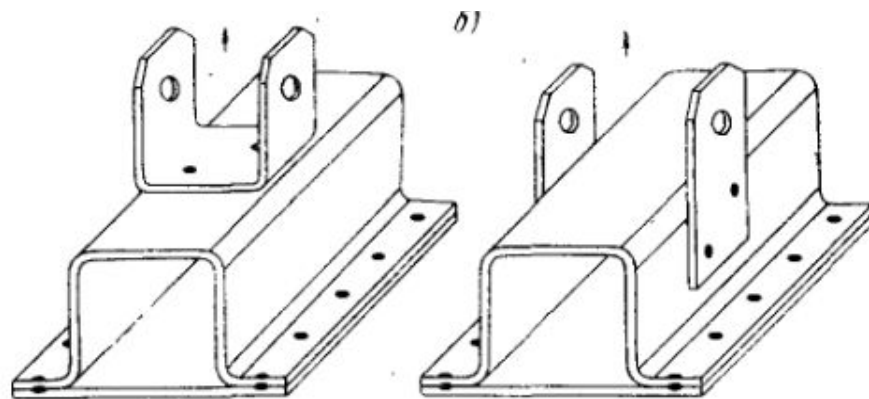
Детали, сваренные точечной сваркой:
